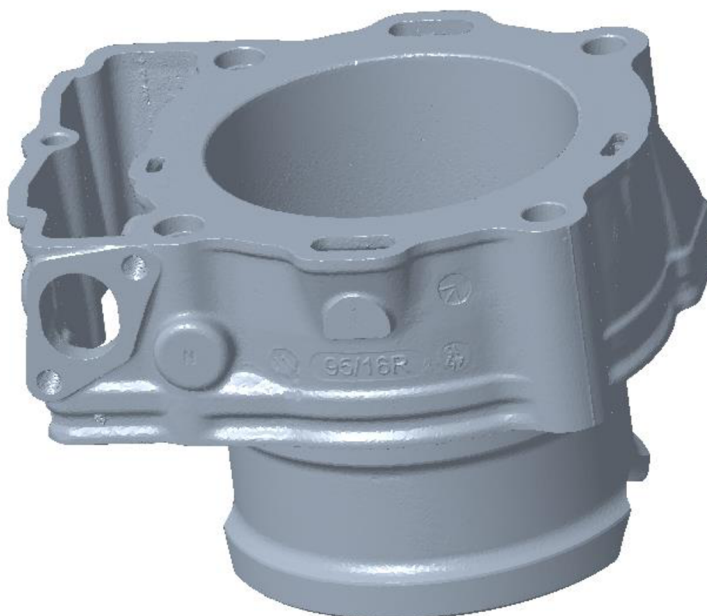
3D sken pravého bloku Husqvarna FE 501
